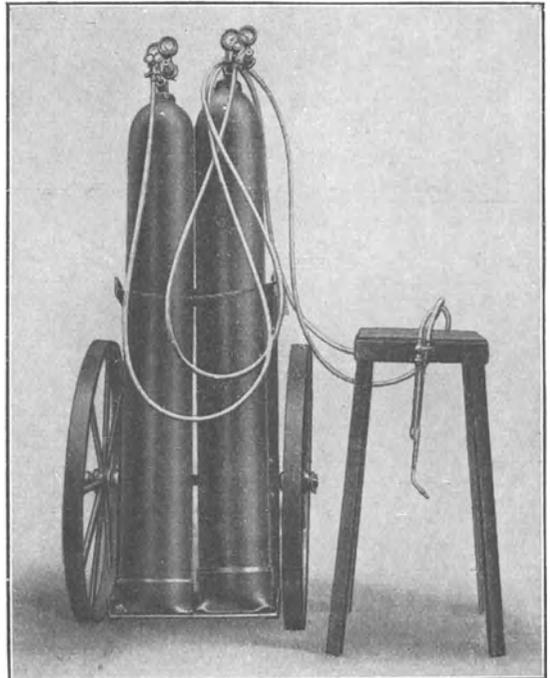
Fährbare Wasserstoffschweißanlage.
